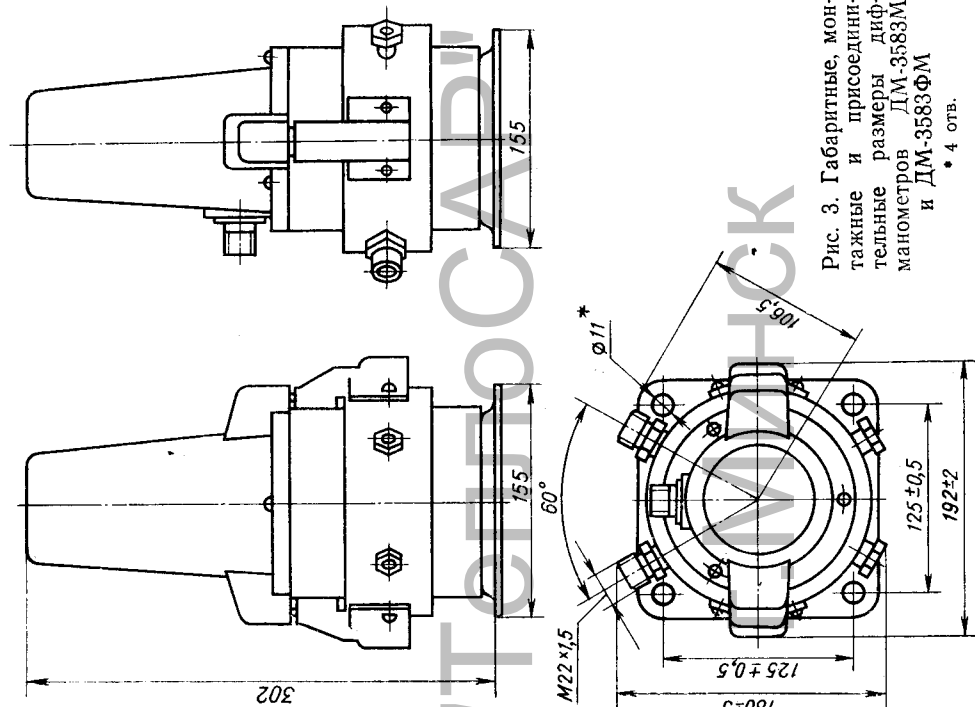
Габаритные, монтажные и присоединительные размеры дифманометров ДМ-3583М и ДМ-3583ФМ
